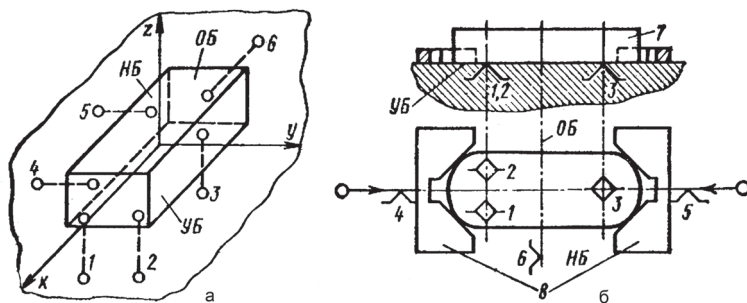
Схемы базирования (а) и установки (б) заготовки на шесть опорных точек:
